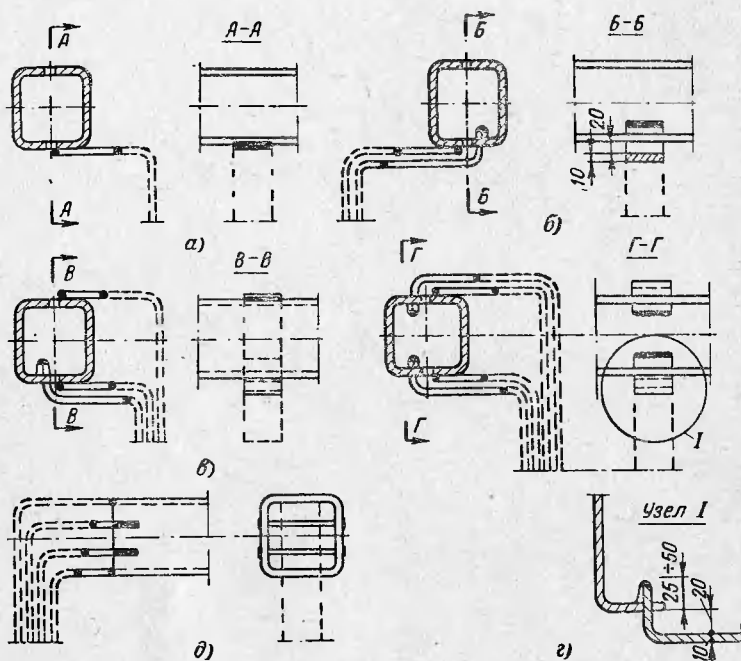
Сварные соединения плоских шин с коробчатыми.
